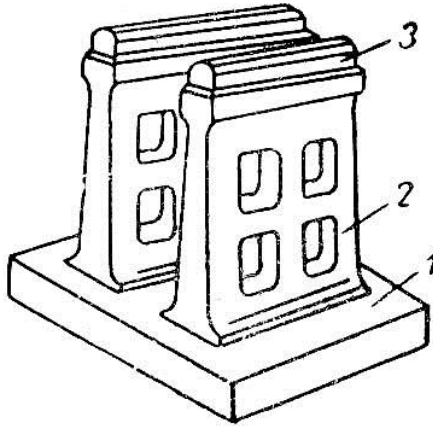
Паралельні бруси для балансування робочого колеса:
